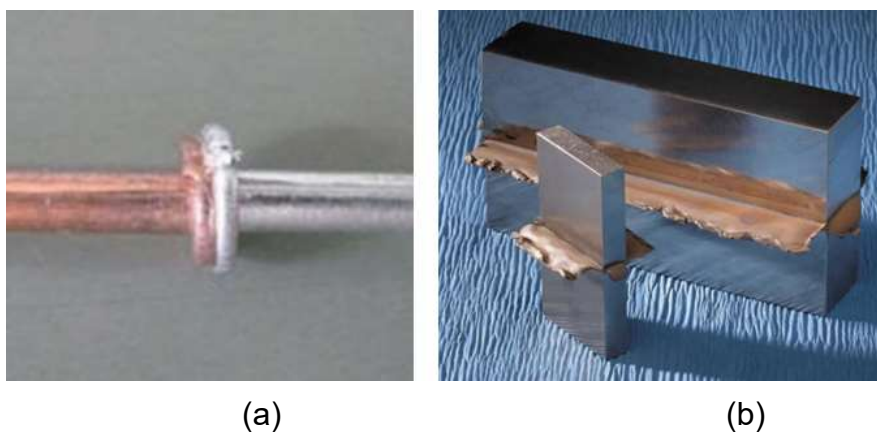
Exemplos de juntas produzidas por (a) soldagem a frio [2] e (b) soldagem por fricção [8].
